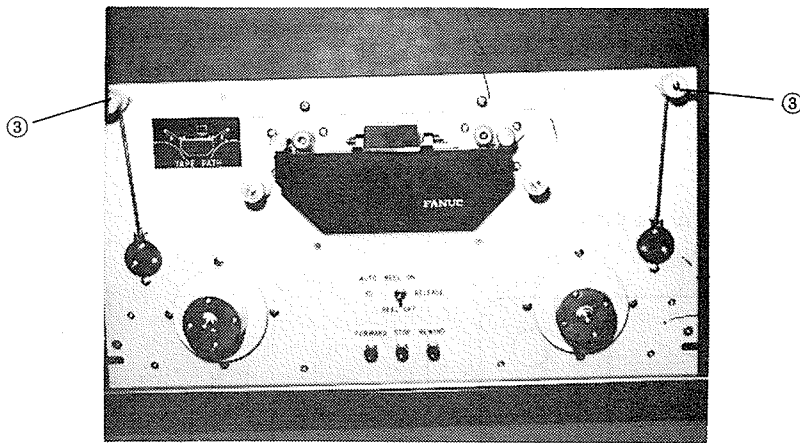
(б) Передний вид ленточного считывателя с бобинами
